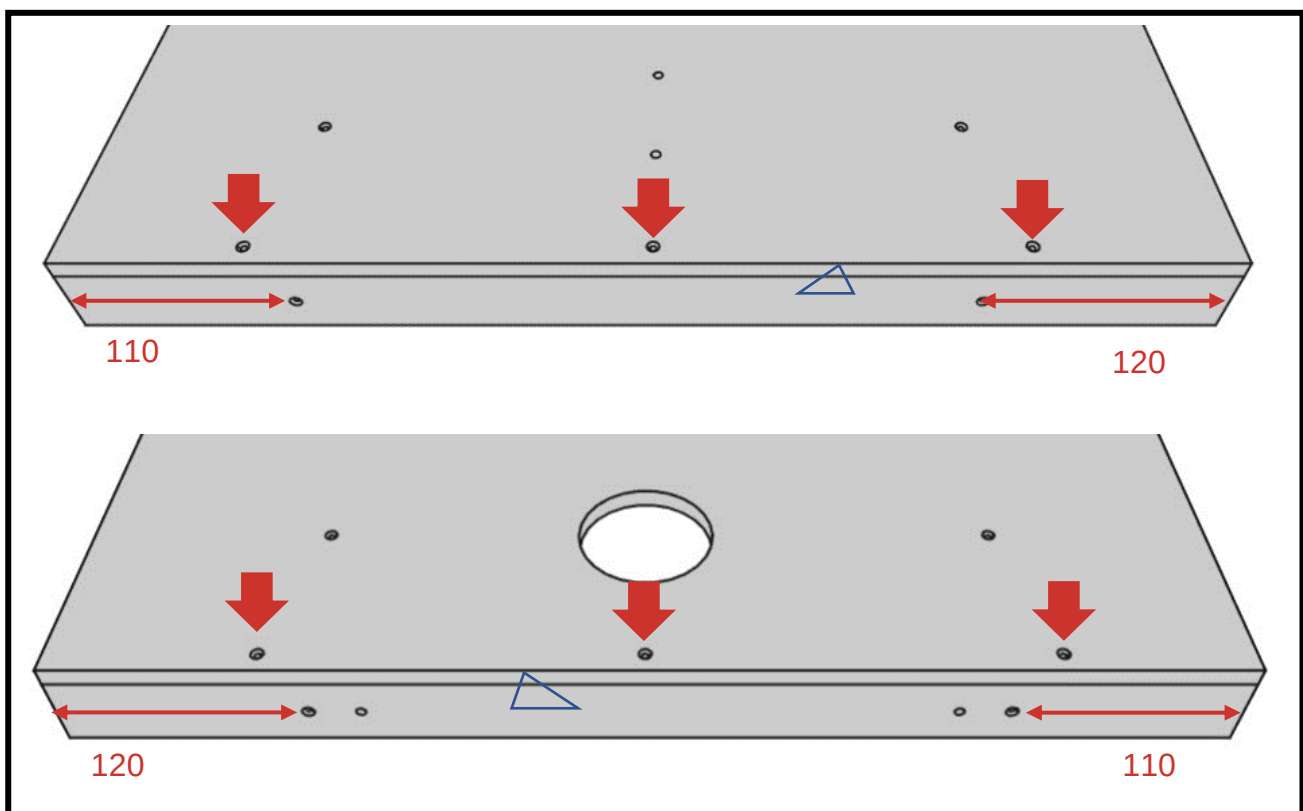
Ausrichtung und Position Längsleisten und Schraubenpositionen
